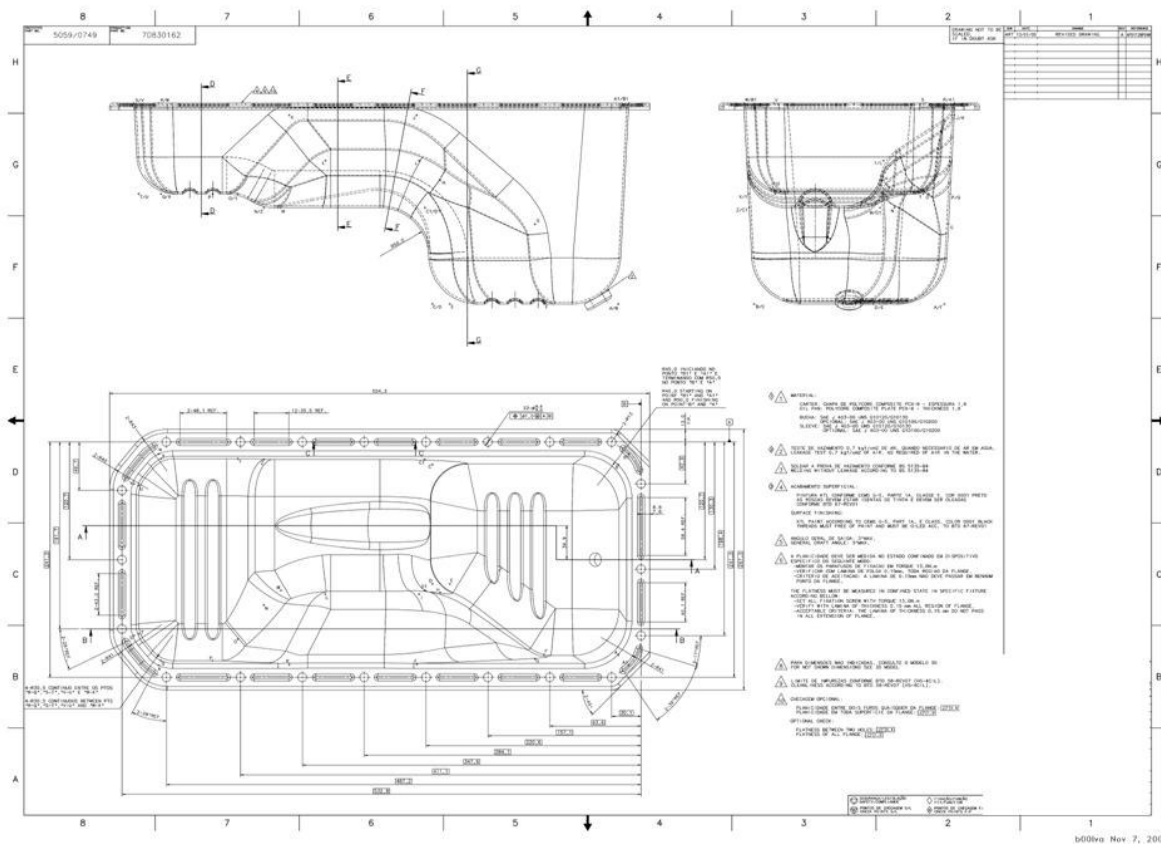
Desenho do cárter de óleo do motor utilizado nos experimentos aplicado em um motor Diesel High Speed de 3,0L de cilindrada total.
